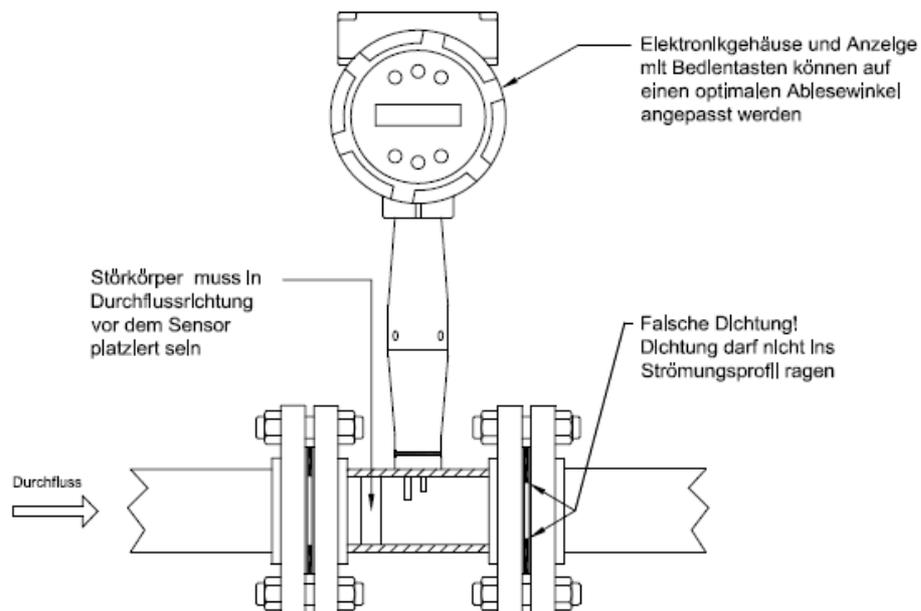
Installation eines Durchflussmessers in Flanschausführung
